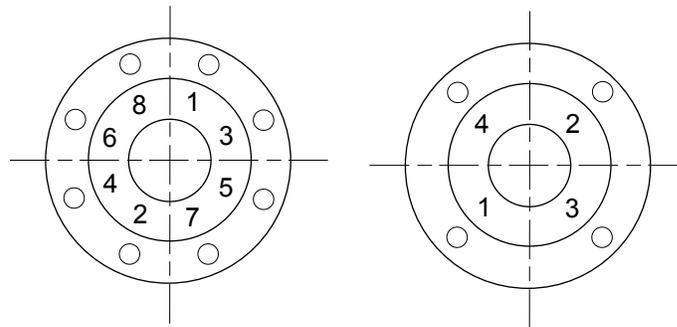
Sequenza di bullonaggio corretta per valvole rivestite di vetro
